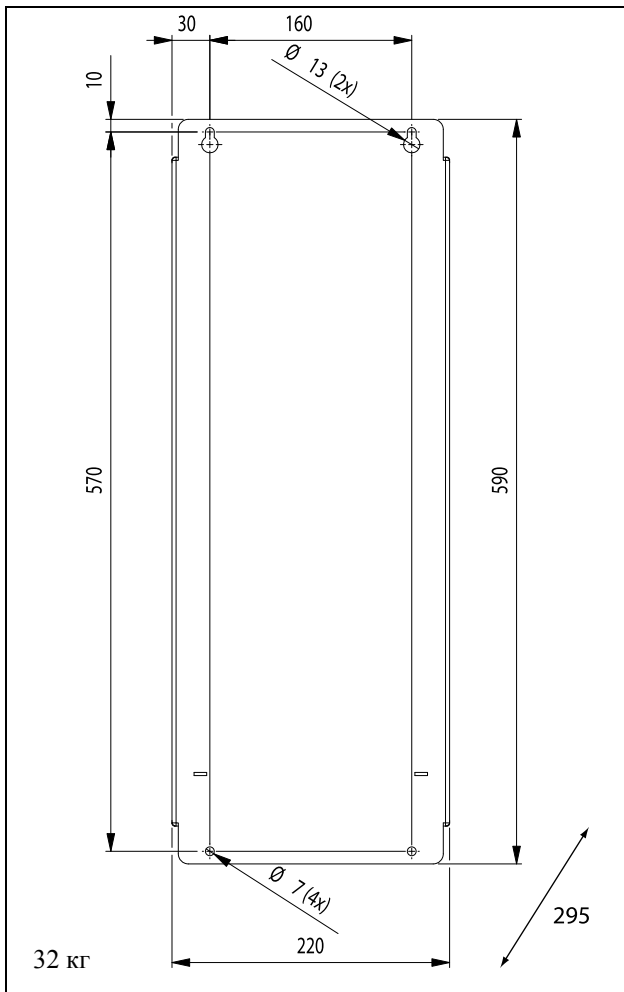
Устройство Emotron FDU моделей 48/52-061 и 074 (типоразмер корпуса D)
